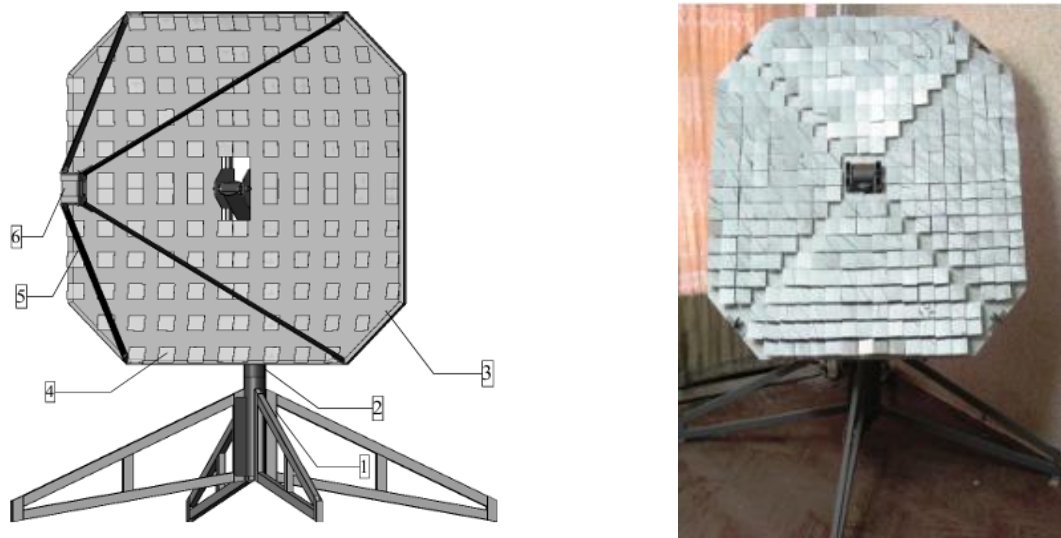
Загальний вигляд експериментального зразка фотоенергетичної установки [7]: 1 - основа з 4 опорами, підшипниковими вузлами для вертикальної осі обертання, редуктором та азимутальним приводом; 2 - поворотна частина з механізмом нахилу, підшипниковими вузлами для горизонтальної осі обертання; 3 - несуча конструкція концентратора; 4 - елемент концентратора - орієнтоване дзеркало (показано приблизно 30% усіх дзеркал); 5 – стрижні підвісу фотоенергетичного блока; 6 - фотоенергетичний блок
